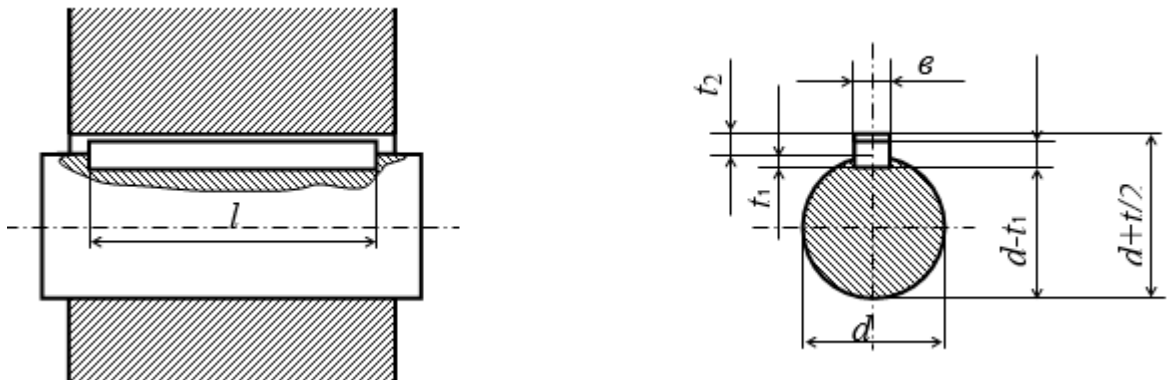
Схема для розрахунку шпонкового з'єднання
